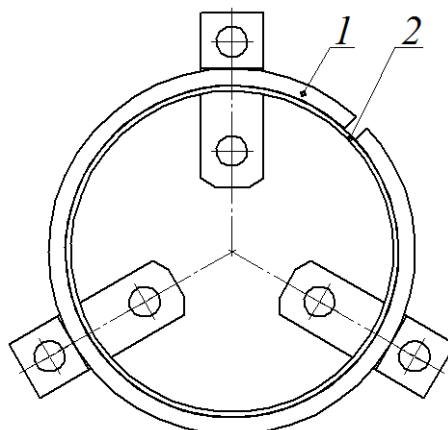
Метод увеличения жёсткости заготовки при помощи разрезной втулки
